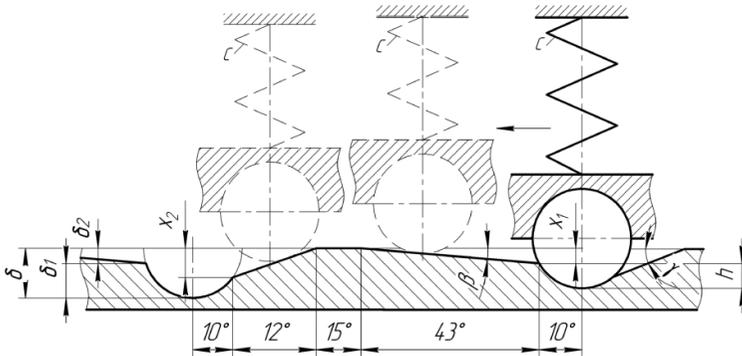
Схема розгортки робочої поверхні ведучої півмуфти
